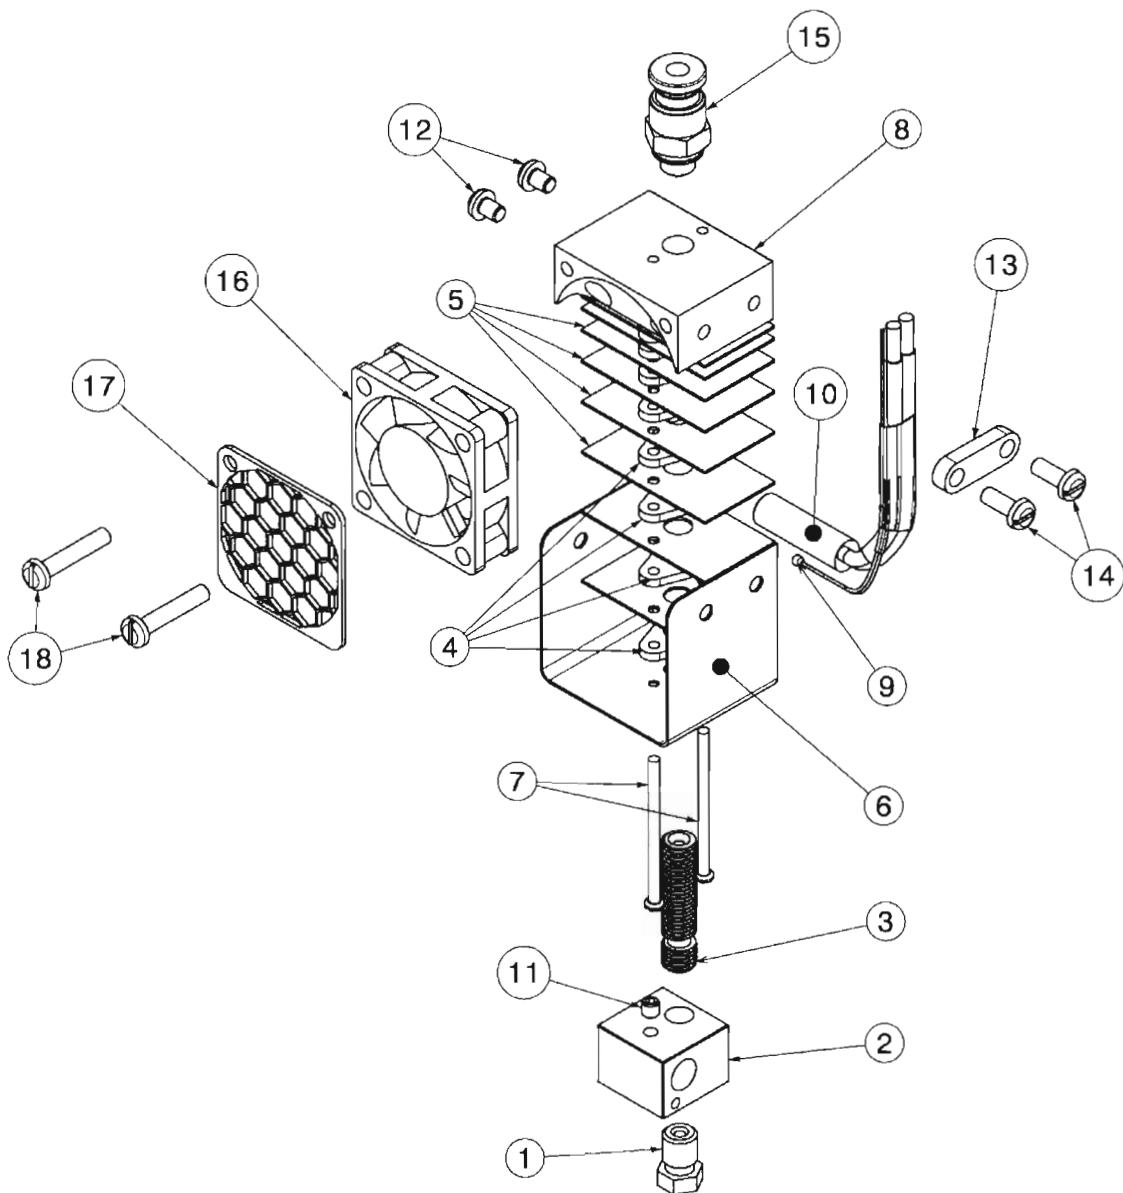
Ansamblul cap imprimare, echipat cu radiator bimetalic în sistem Bowden, vedere explodată
